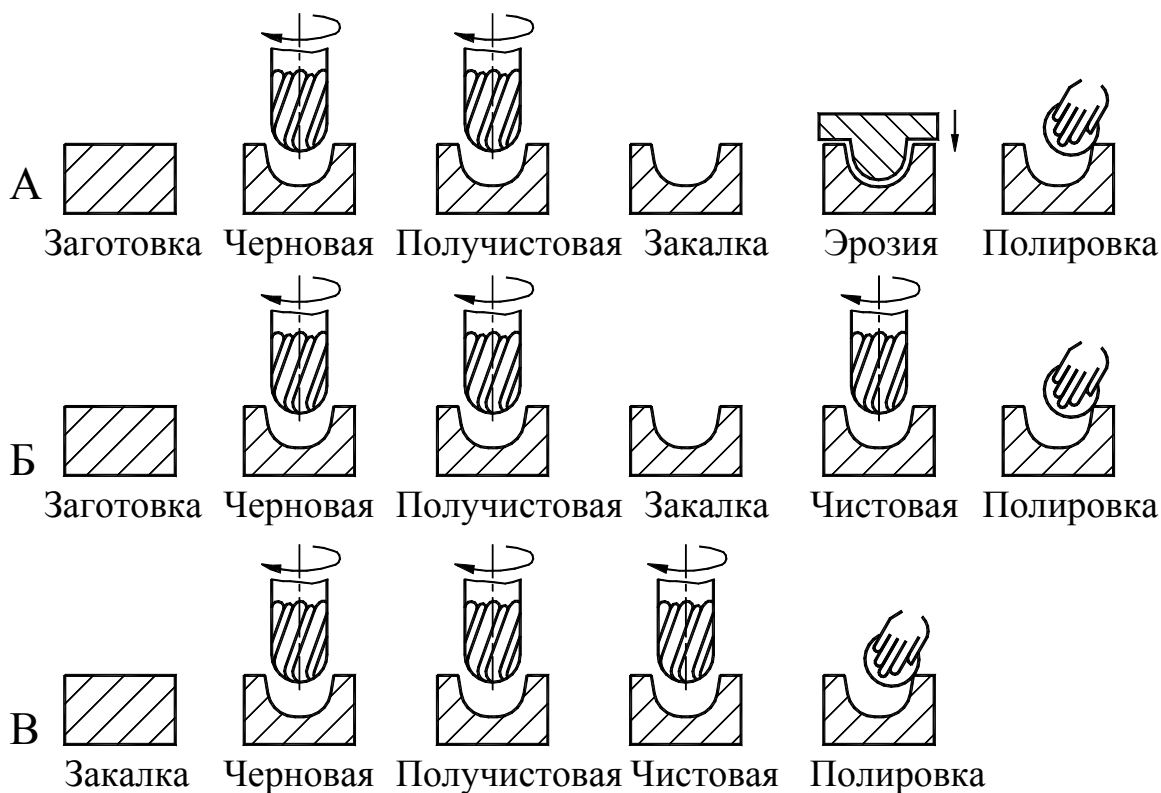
Упрощение производственного процесса изготовления формообразующих элементов оснастки (пресс-формы, штампы) при использовании высокоскоростной обработки [10]: А – обычный техпроцесс; Б – ВСО с закалкой внутри техпроцесса; В – ВСО с закалкой заготовки
